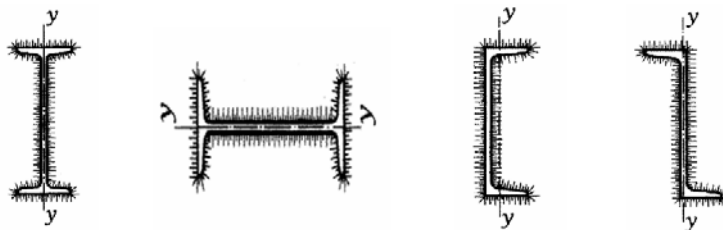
TORSIÓN Y CORTANTE COMBINADOS SOBRE PERFILES CON SOLDADURA PERIMETRAL
